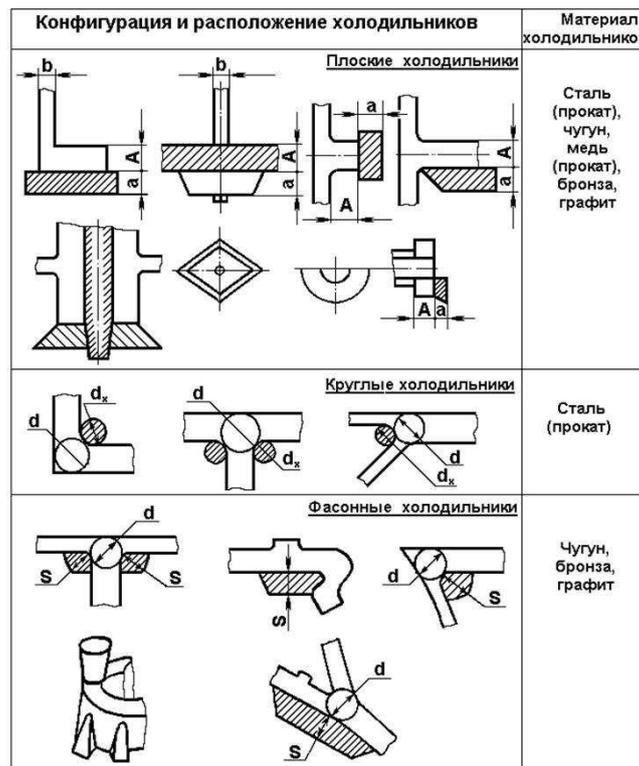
Схемы применения плоских, круглых и фасонных наружных холодильников
